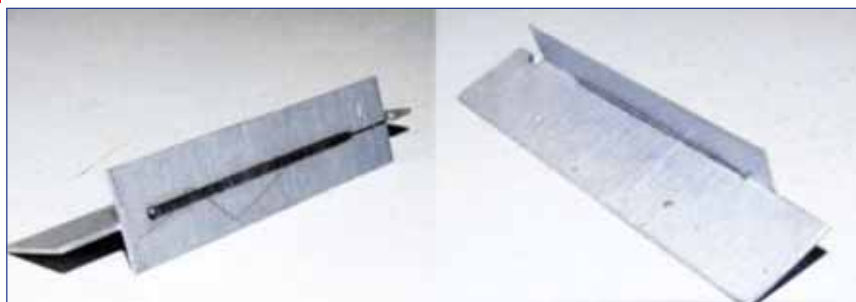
Образец сварки алюминиевого сплава толщиной 0,3 мм. Мощность волоконного лазера 700 Вт, скорость сварки около 1 м/мин
